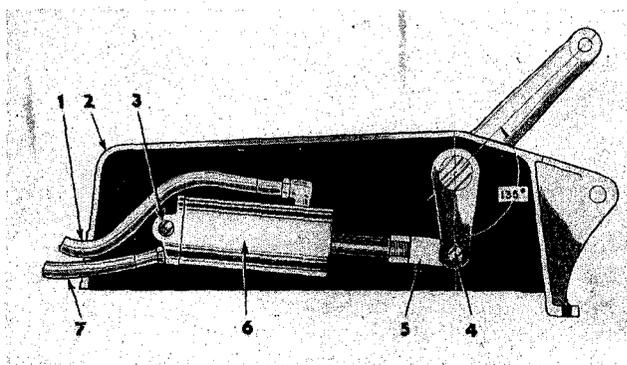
Hauptgehäuse und hydraulischer Zylinder
